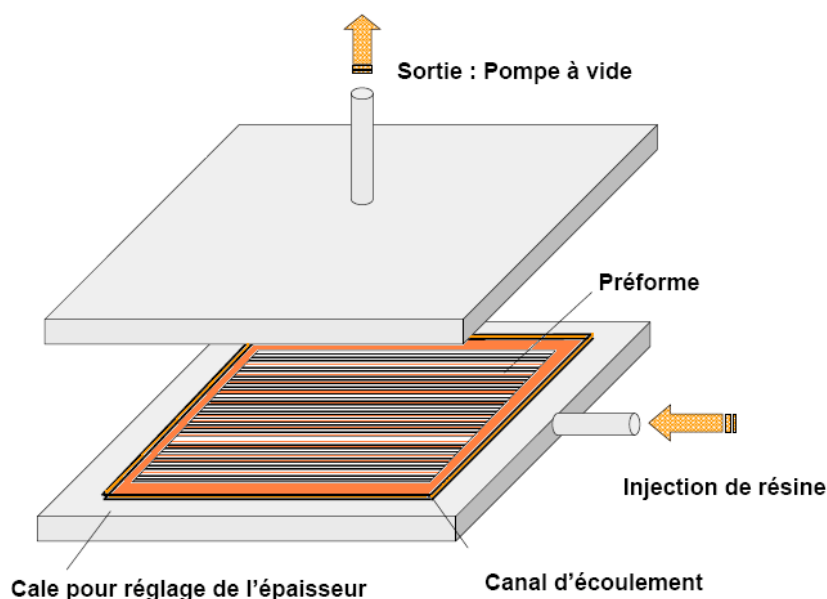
Procédé RTM : *Resin Transfer Molding
